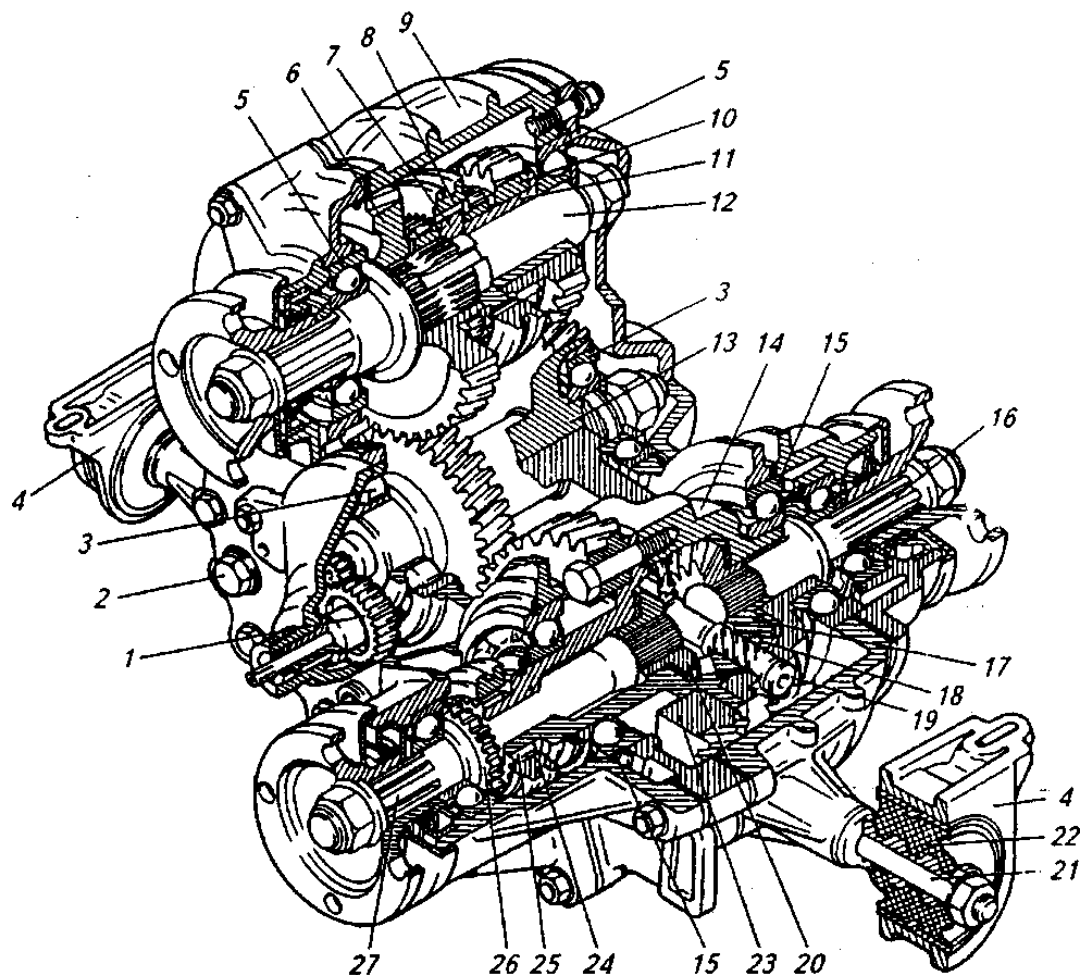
Раздаточная коробка автомобиля ВАЗ-21213: 1 — привод спидометра; 2 — пробка для заливки и контроля уровня масла; 3, 5 - подшипники соответственно промежуточного и ведущего валов; 4— кронштейны подвески раздаточной коробки; 6,10— зубчатые колеса соответственно высшей и низшей передач; 7, 8 — соответственно ступица и скользящая муфта переключения передач; 9— корпус; 11 — втулка; 12— ведущий вал; 13— промежуточный вал; 14— корпус дифференциала; 15— подшипники корпуса дифференциала; 16, 27— валы привода соответственно заднего и переднего мостов; 17, 20— зубчатые колеса привода соответственно заднего и переднего мостов; 18— сателлит; 19 — ось сателлитов; 21, 22—соответственно ось и резиновая подушка подвески раздаточной коробки; 23 — ведомое зубчатое колесо; 24 — скользящая муфта блокировки дифференциал; 25 — зубчатый венец корпуса дифференциала; 26— зубчатое колесо вала привода переднего места
